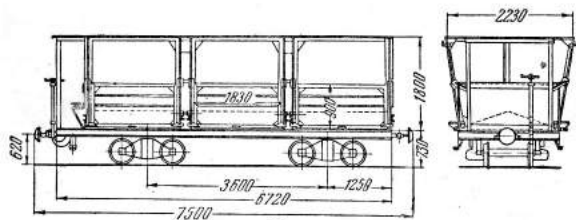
Металлический полувагон для торфа типа УМВ.
